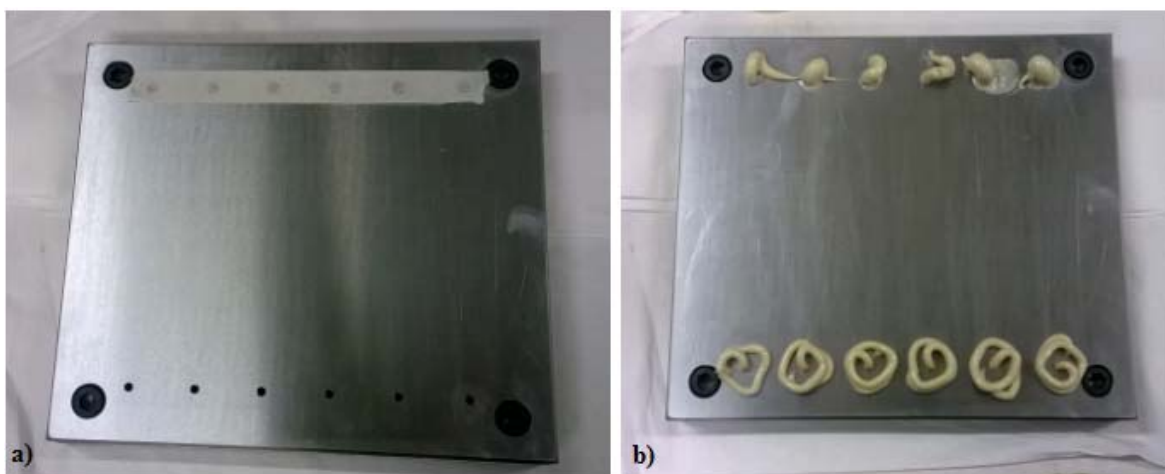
Fecho do molde: a) Colocação da placa superior do molde e b) aperto do molde
